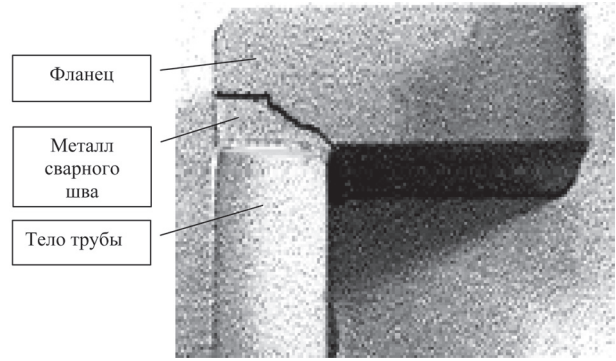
Характер разрушения сварного кожуха корпуса водила, выполненного из стали 35
